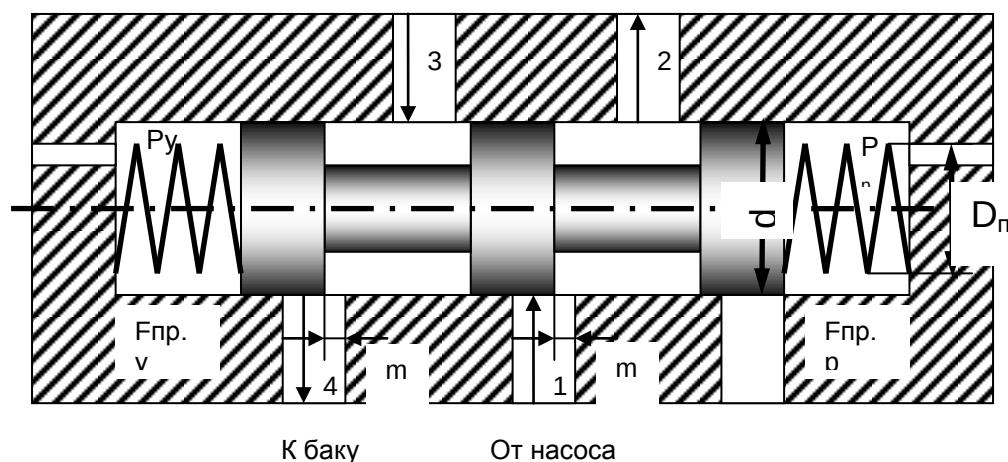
Расчетная схема золотника регулятора: 1- напорный канал; 2 – канал идущий к двигателю подачи; 3- канал идущий от двигателя подачи; 4- сливной канал; P_y - канал управления от гидроцилиндра; P_n - канал управления от гидромотора дискового инструмента.
